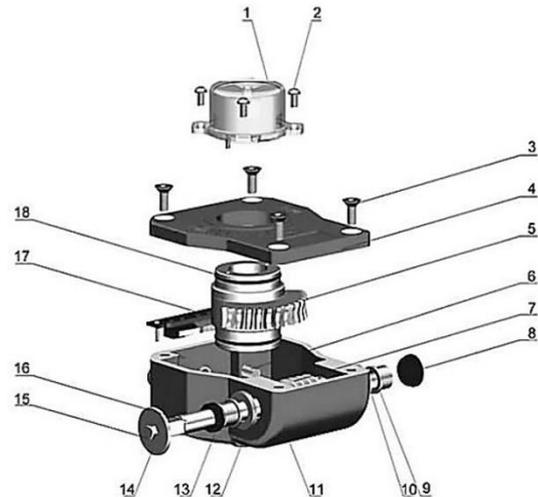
Редуктор четвертьоборотный с концевыми выключателями.
